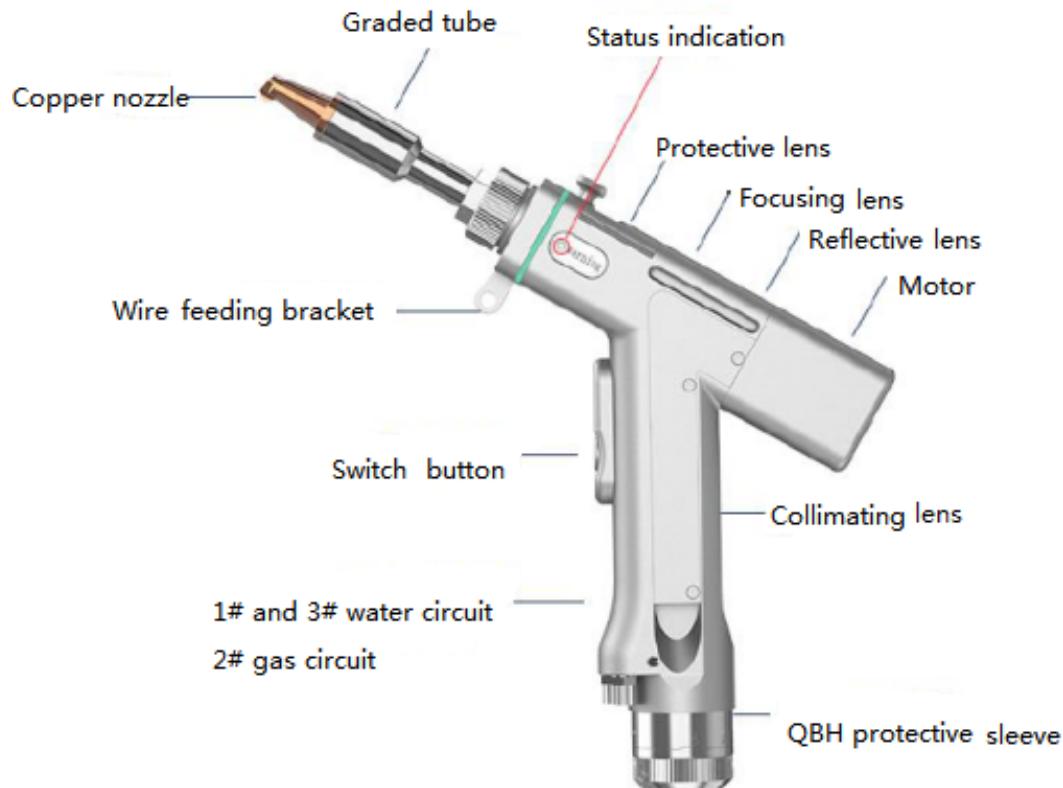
Schéma de la torche de soudage laser manuelle
